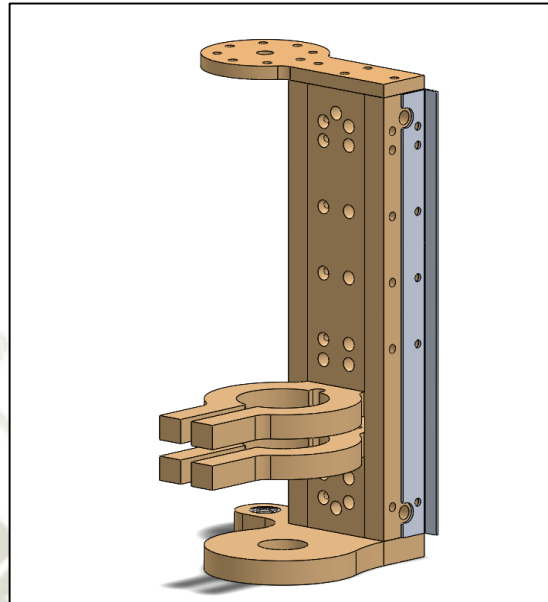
Diseño 3D Conjunto carro Eje Z.
